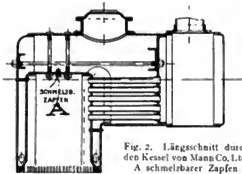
Längsschnitt durch den Kessel von Mann Co. Ltd. A schweißbarer Zapfen
